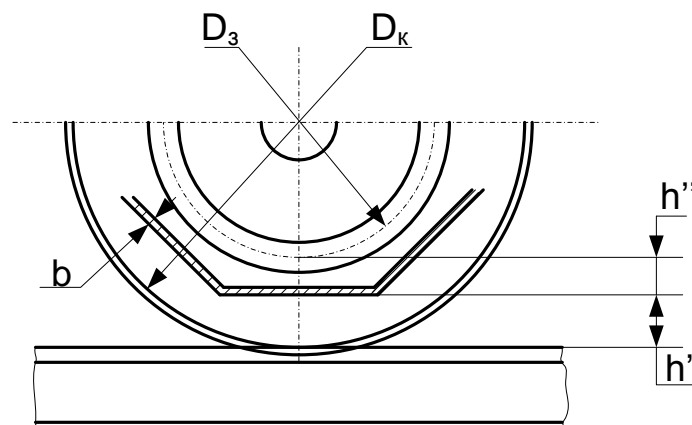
Эскиз к определению размеров зубчатой передачи тягового редуктора
